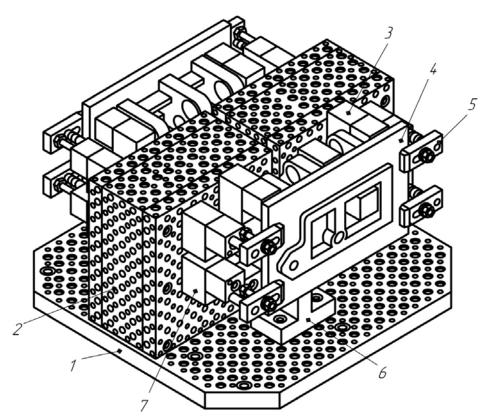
Двухместное гидравлическое приспособление для установки корпусной детали: 1 — плита; 2 — угольник; 3, 6 — опоры; 4 — заготовка; 5 — прихват; 7 — гидроцилиндр
